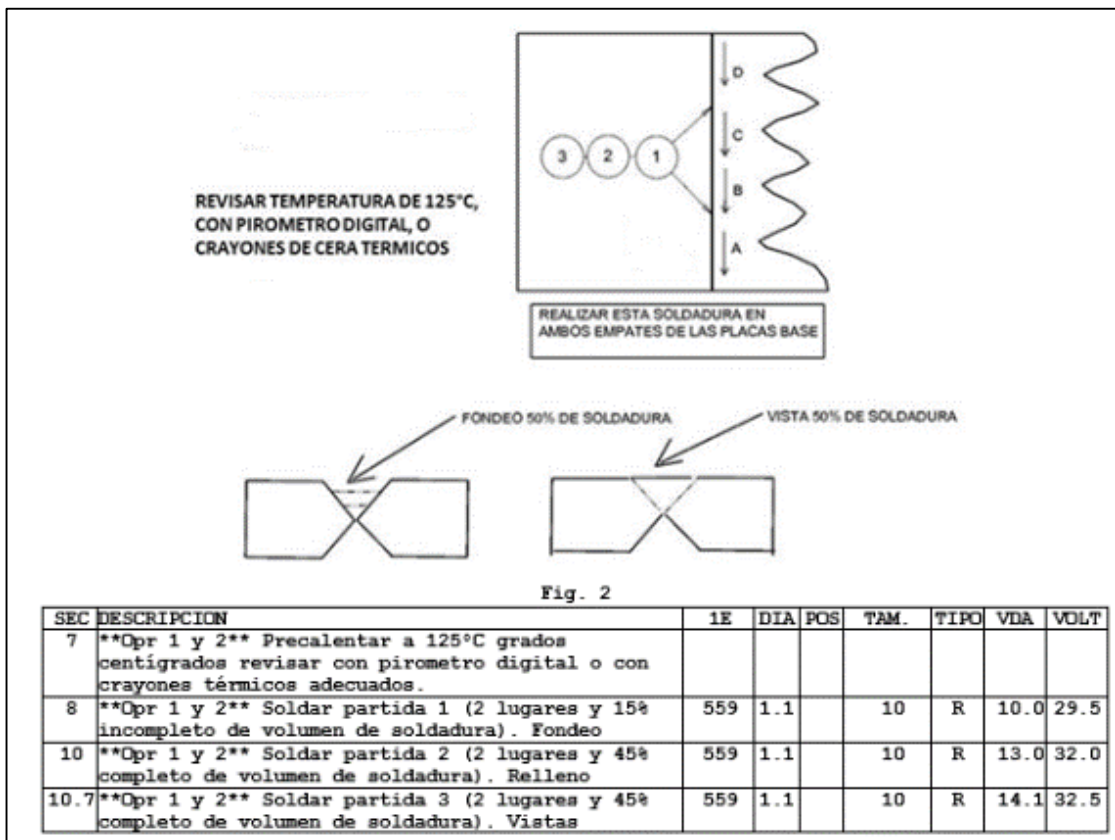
9 Procedimiento de soldadura final del primer lado de pisos Hardox 450 de caja para camión minero (cortesía de la compañía fabricante de cajas para camión).
